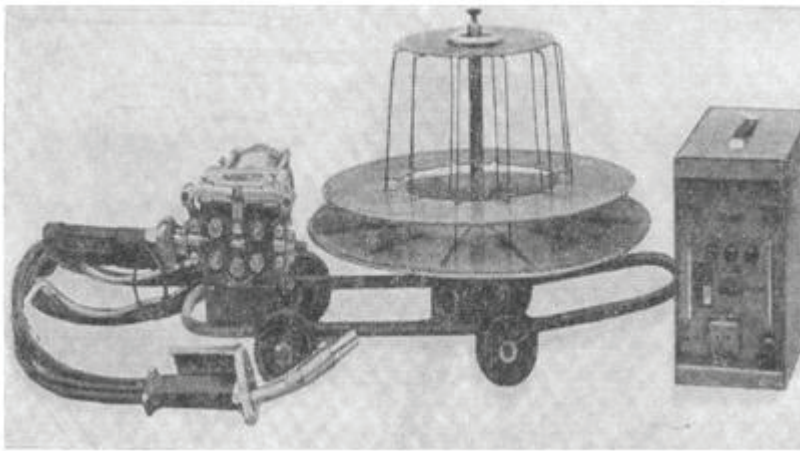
Полуавтоматы для сварки и наплавки:
